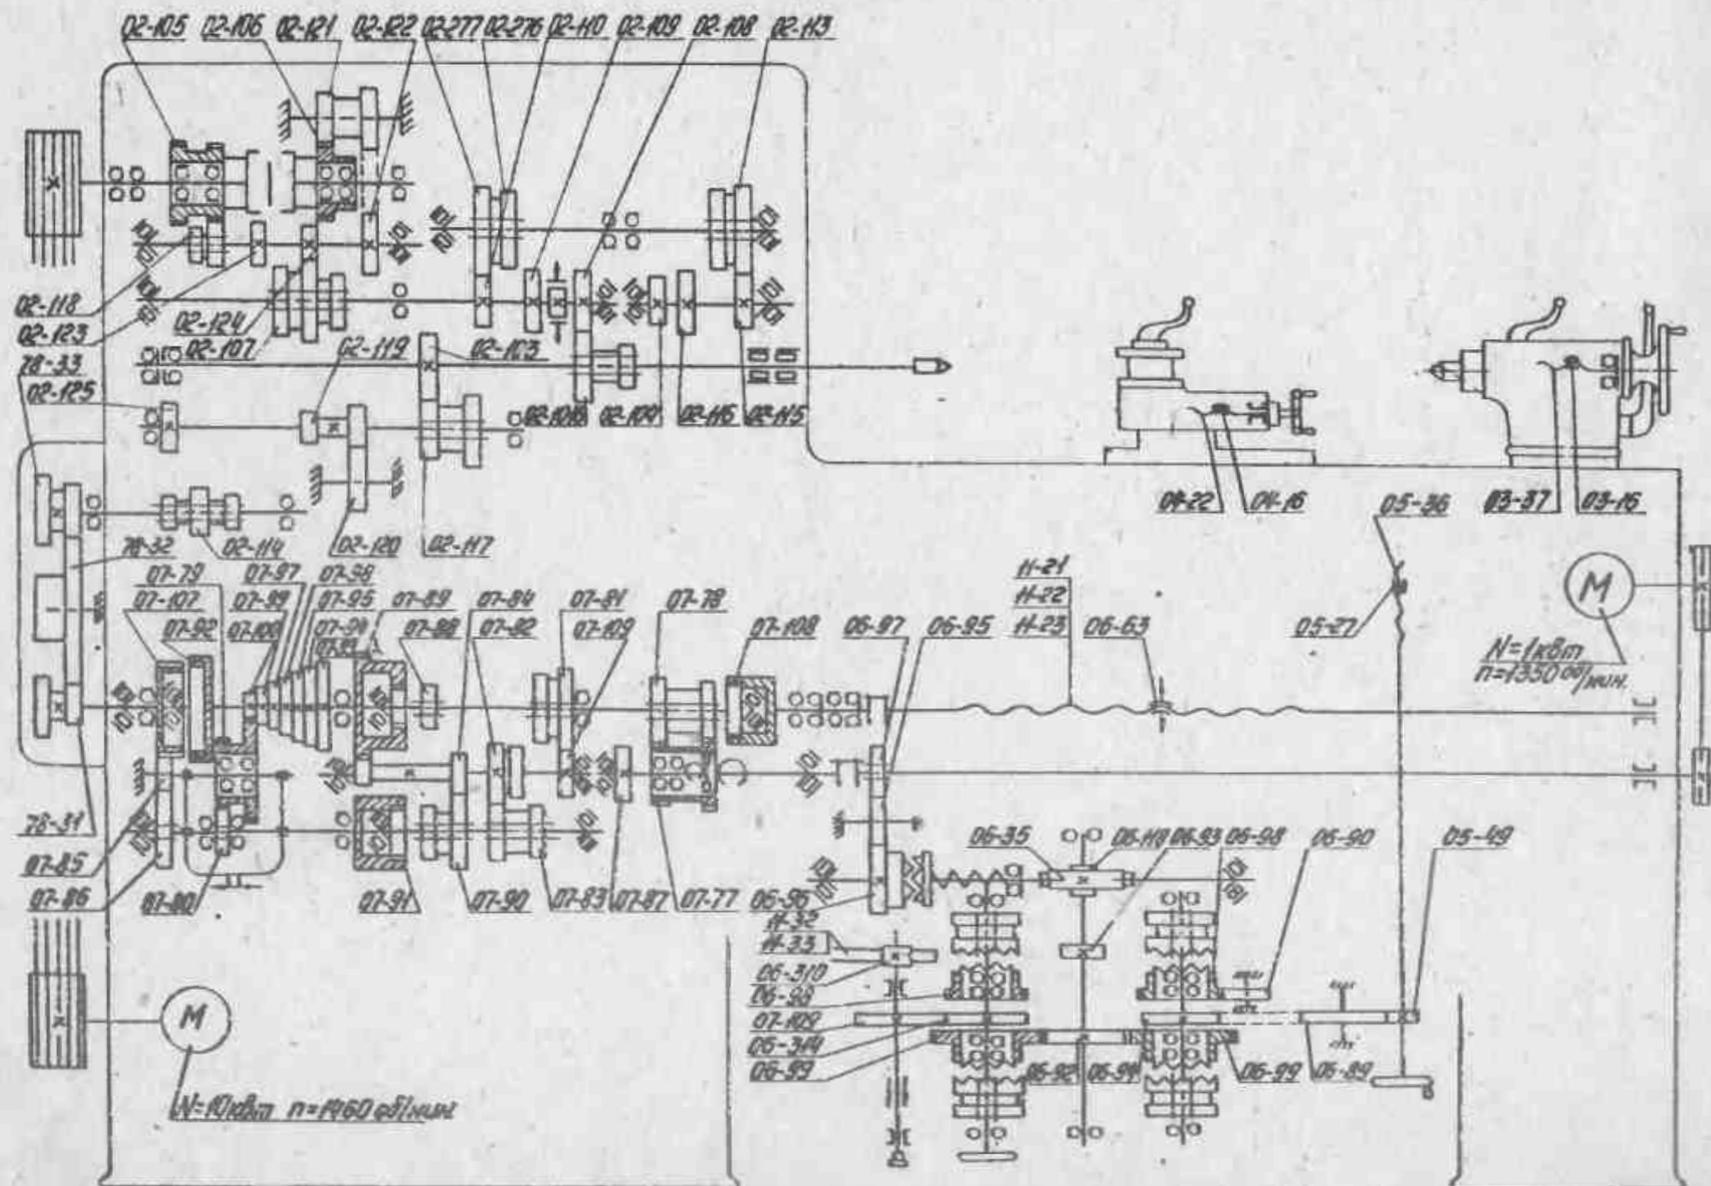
Кинематическая схема станков 1К62 и 1К625
